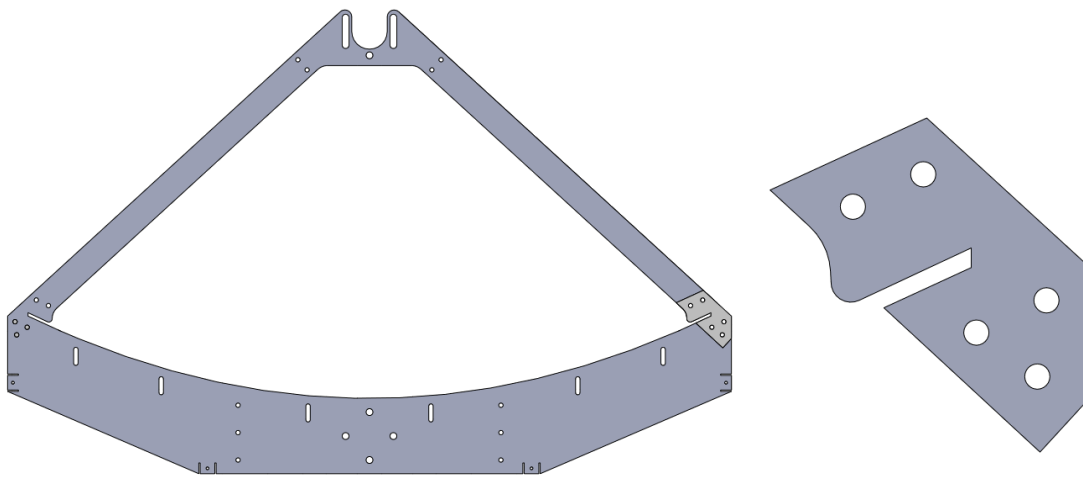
Diseño de la parte "A" o eje de giro del buje (izquierda) y parte "B" o plato del buje(derecha).
